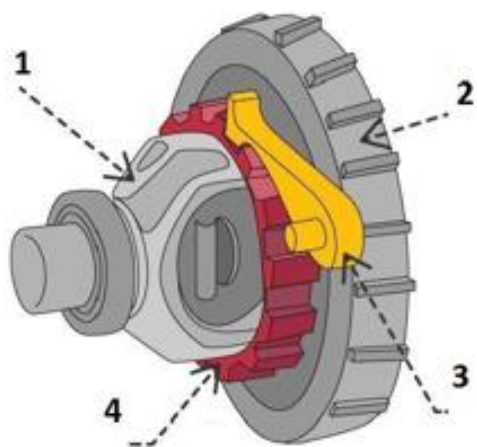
Устройство стояночной тормозной системы: *1* – корпус дифференциала; *2* – планетарная шестерня; *3* – блокирующий рычаг; *4* – стопорная шайба
